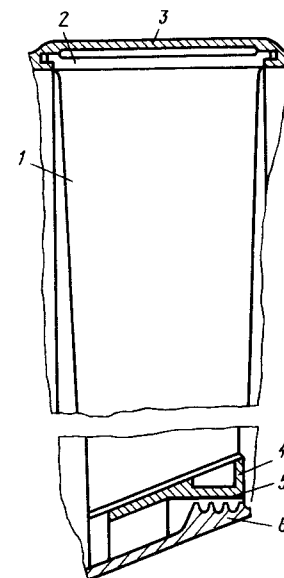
Лопатка направляющего аппарата с двухсторонним креплением:
